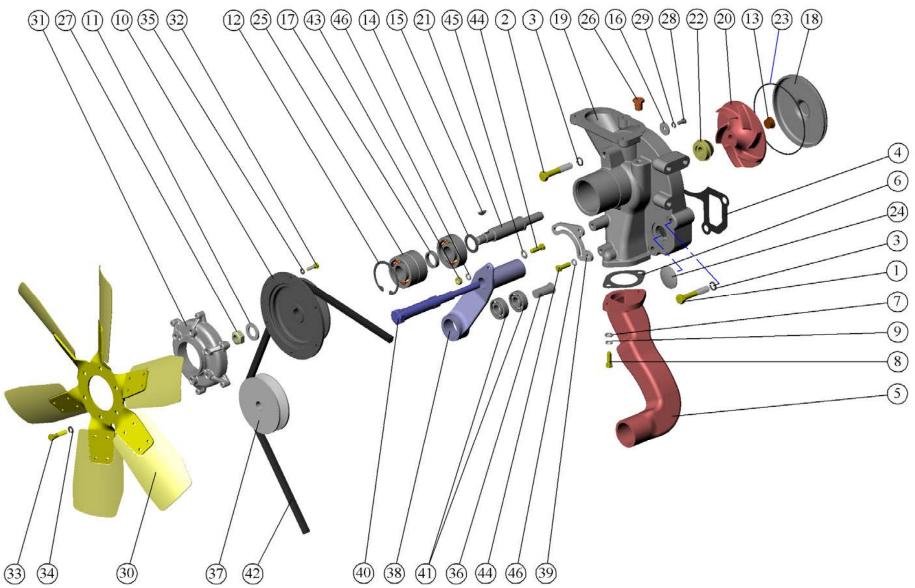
Насос водяной. Установка вентилятора. Установка натяжителя. Fig. 13 Water pump. Fan installation. Tension mechanism installation.
